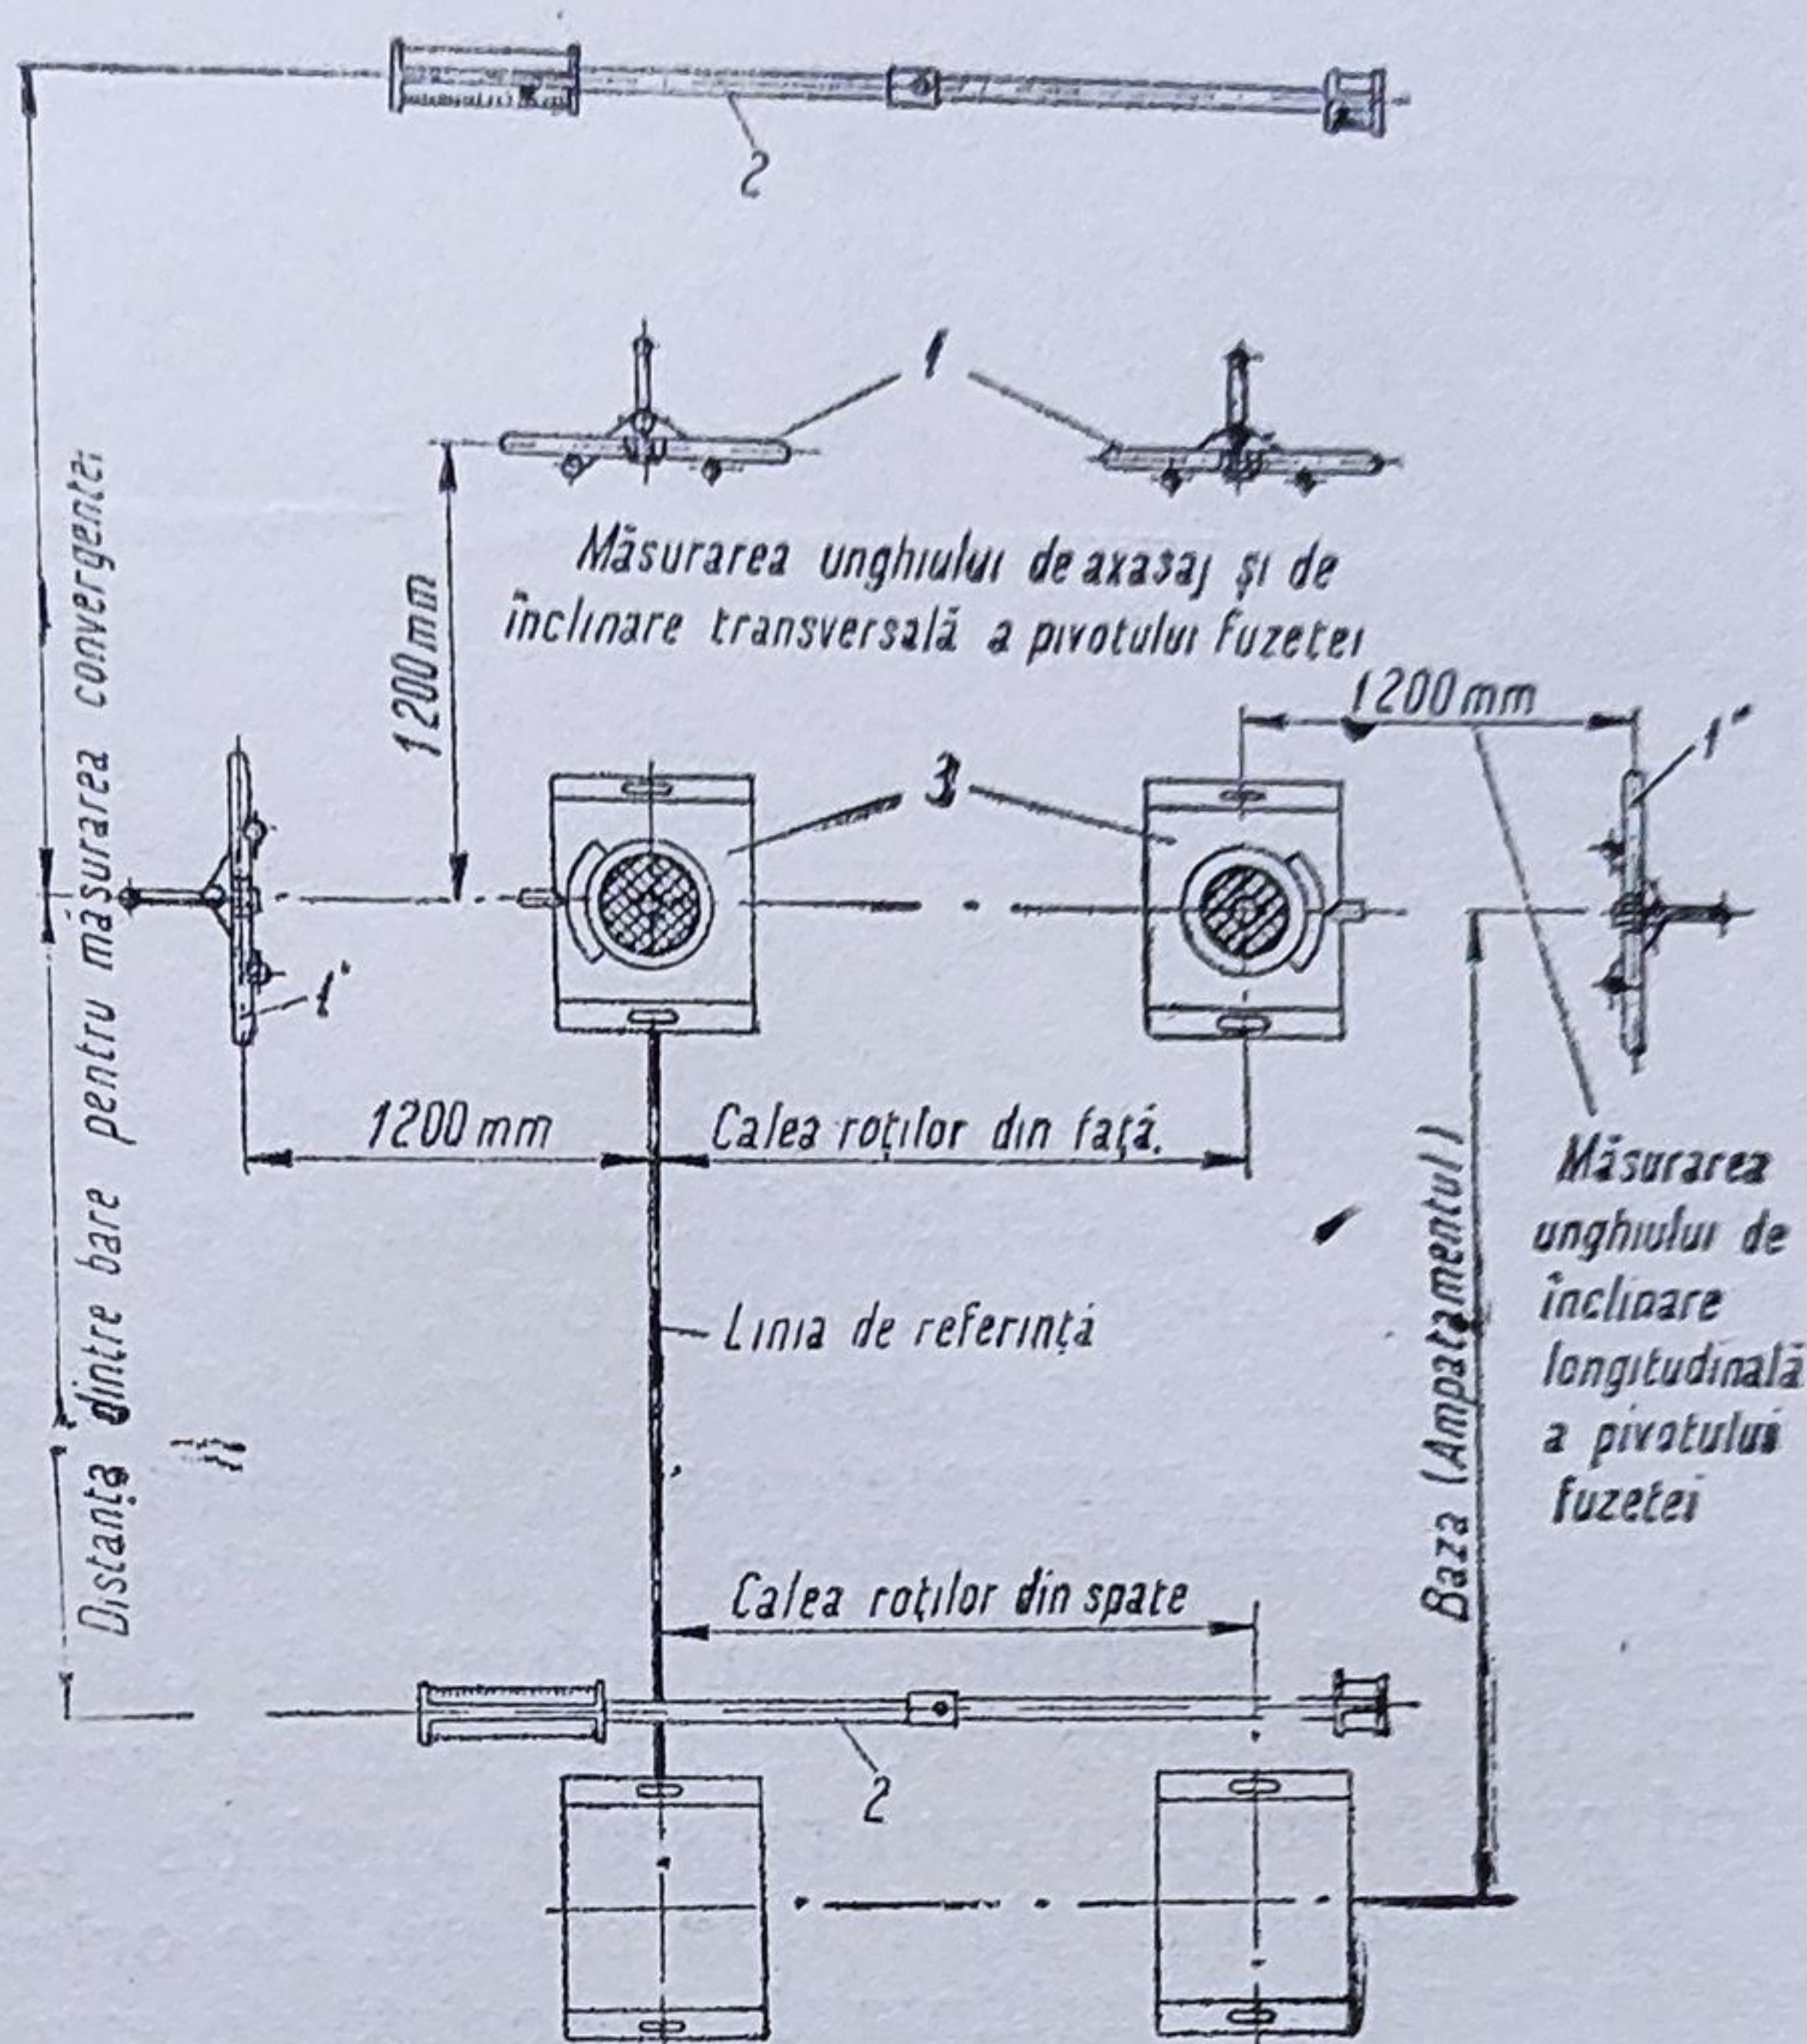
Elementele instalației de măsurare a unghiurilor roților de direcție.
